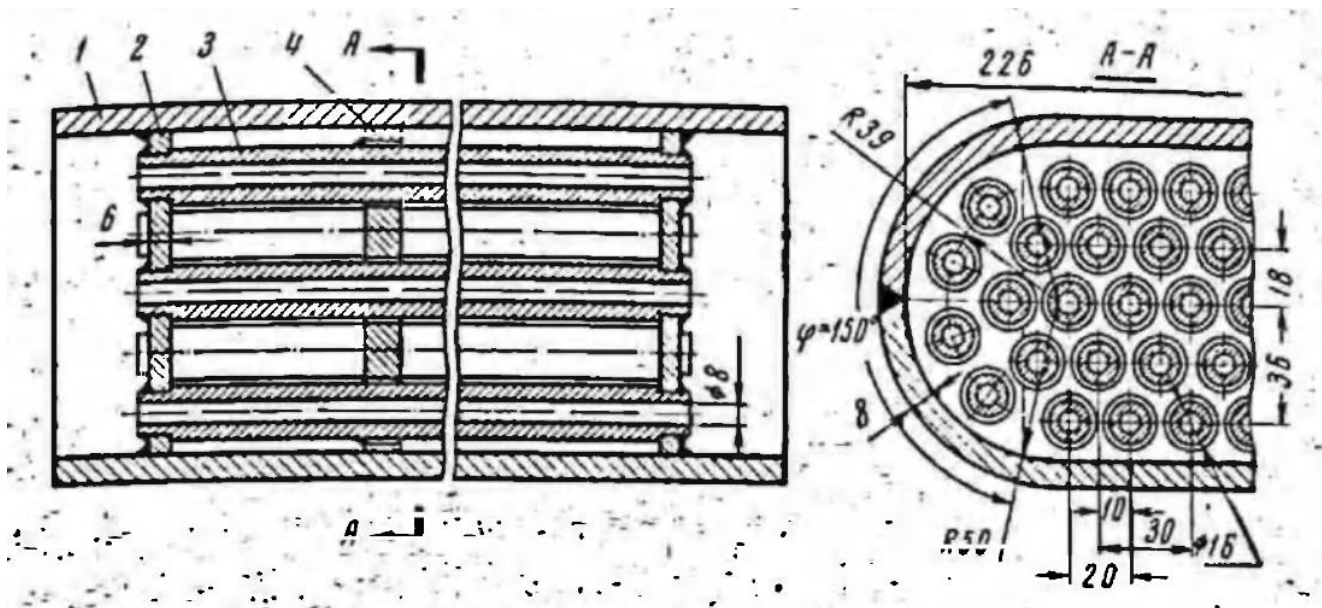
Зварний вузол маслоохладжувача [16]: 1 - корпус; 2 - кришка; 3 - трубка; 4 - перегородка
